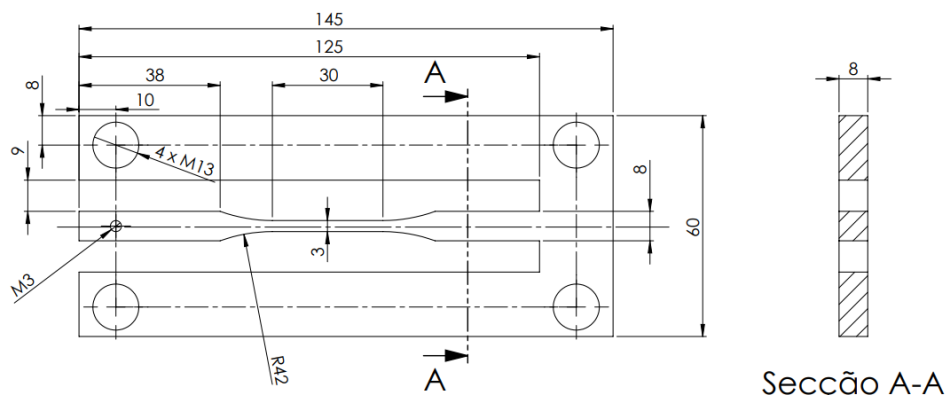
Componente 1 da moldura de fixação para corte de provetes do ensaio de tração uniaxial.
